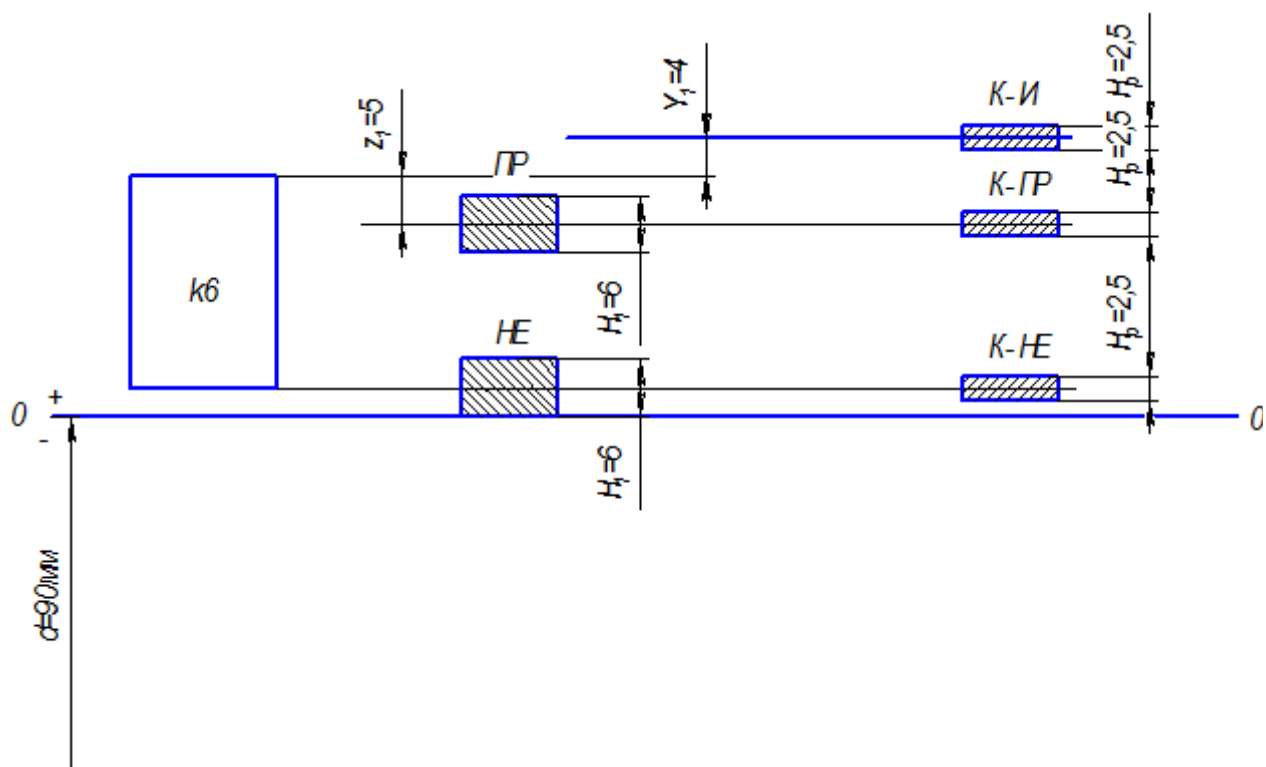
Схема расположения полей допусков калибров и контркалибров для $d=90k6$
